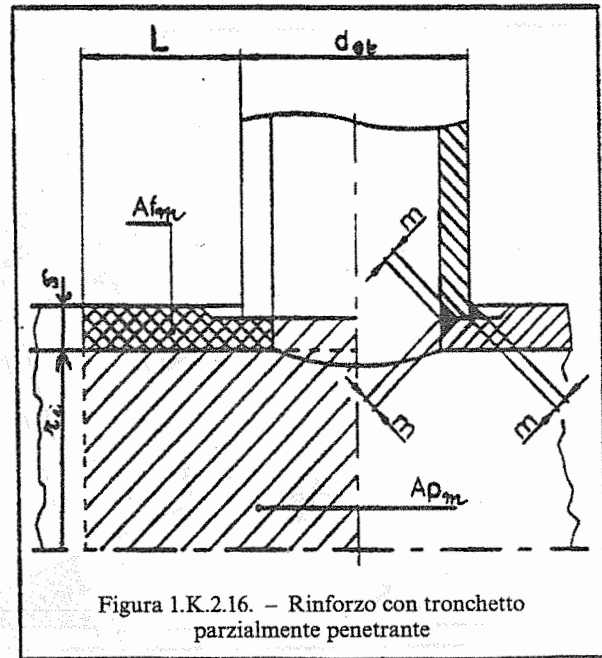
K.2.16. - Rinforzo con tronchetto parzialmente penetrante
